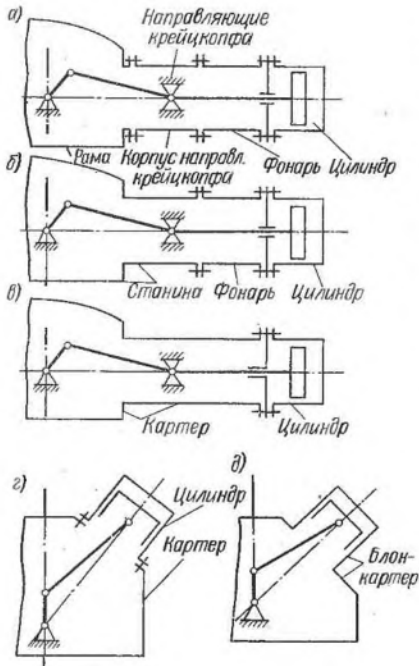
Схемы исполнения корпусных деталей компрессора с базовым элементом: а — рама; б — станина; в, г — картер; д — блок-картер
